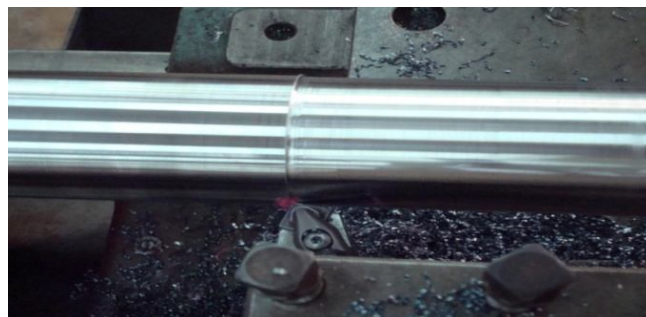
Usinage d'une ébauche XC32 par une plaquette en carbure cémenté
